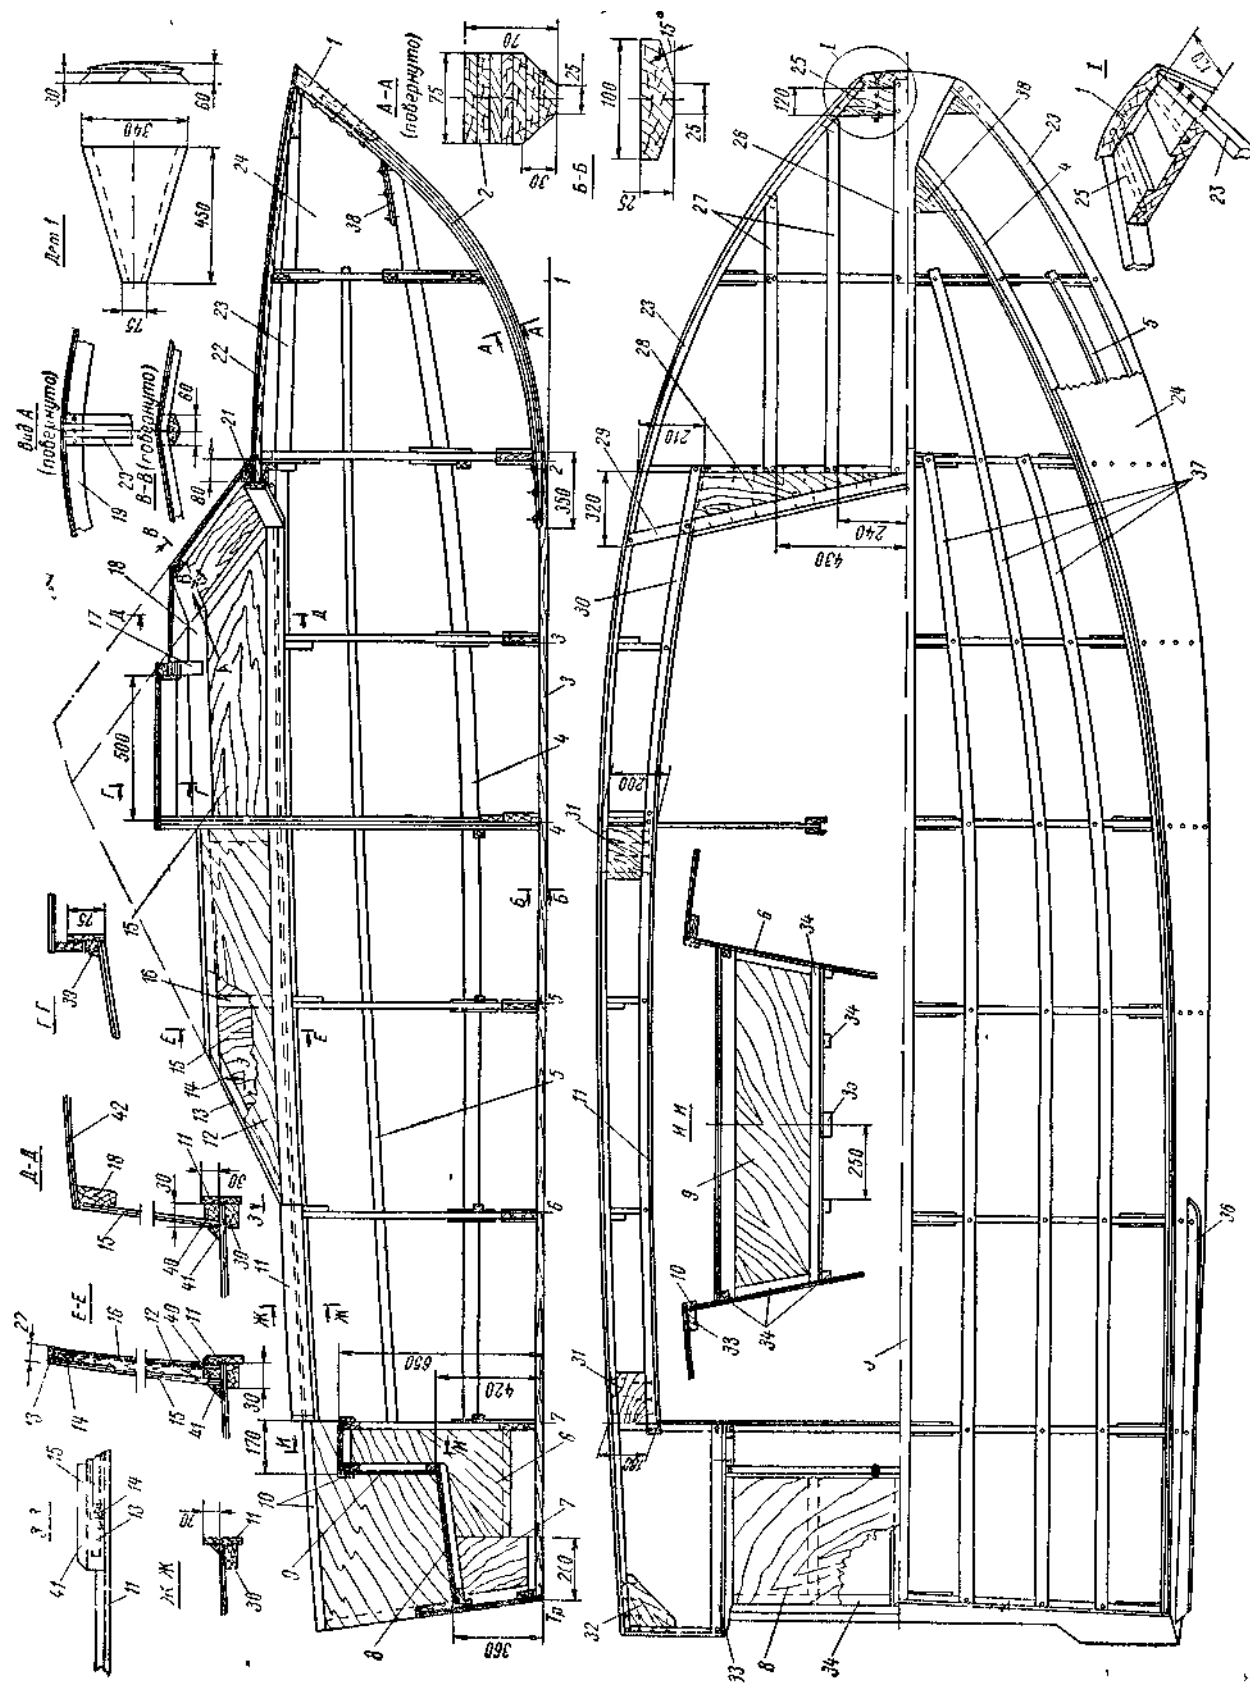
Конструктивный чертеж корпуса (продольный разрез, план, набор палубы и днища).
